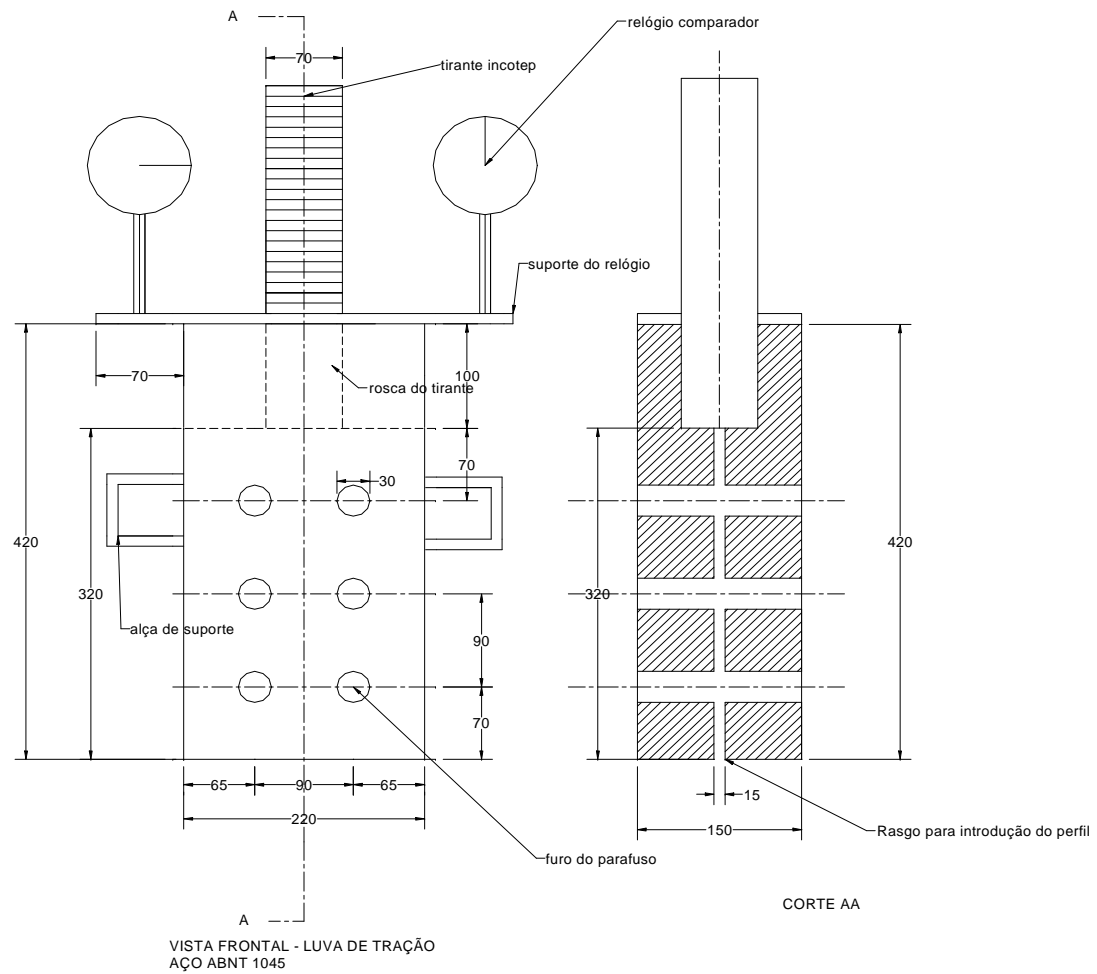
Croqui executivo da garra (dimensões em mm).
